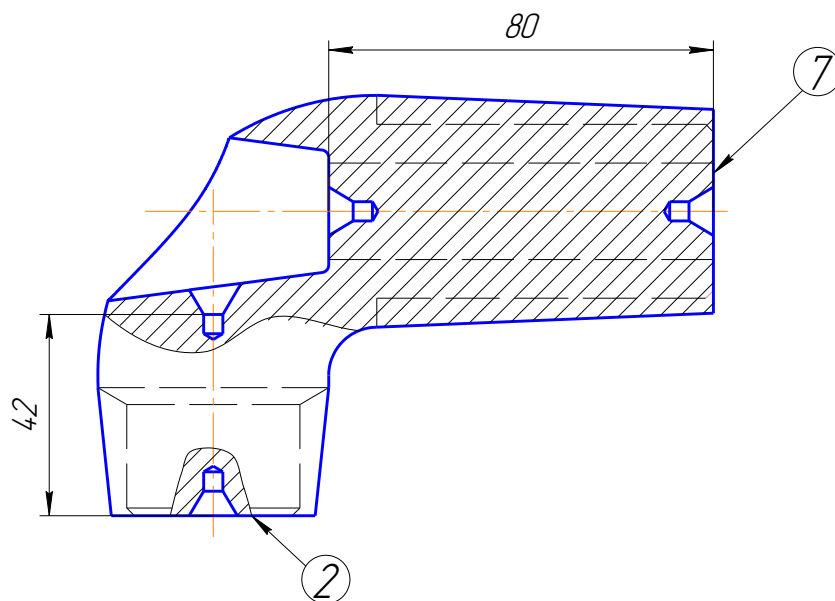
Схематичне зображення фрезерно-центрувальної операції.
